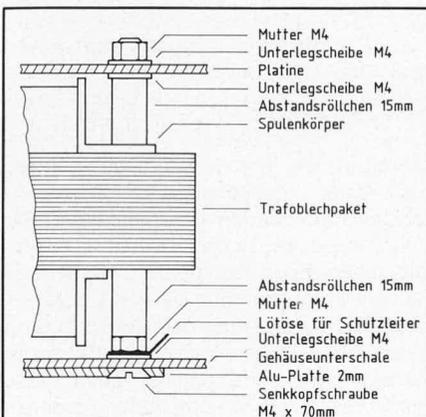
Befestigungsskizze des Netztransformators und der Basisplatte im Gehäuseunterteil
